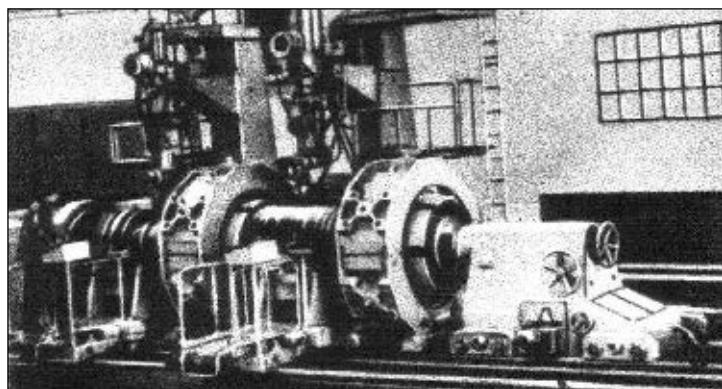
Наплавка валка блюминга на вальценаплавочном станке КЖ–9705
